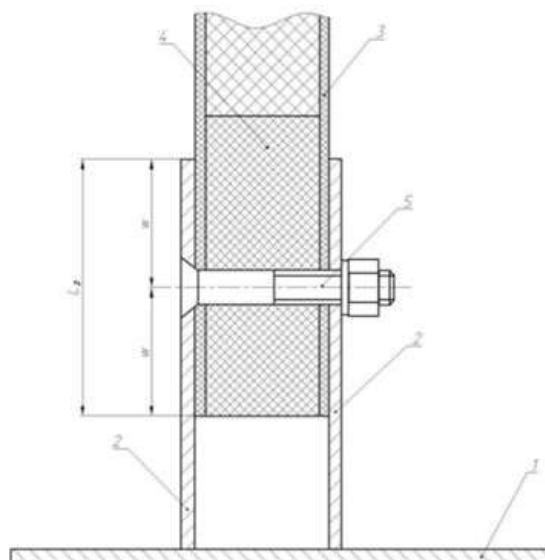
Вузол клеєболтового з'єднання перегородки з металевим корпусом (з двома металевими комінгсами): 1 - палуба корпусу; 2 - комінгси; 3 - перегородка; 4 - пінопласт підвищеної густини; 5 - болт
